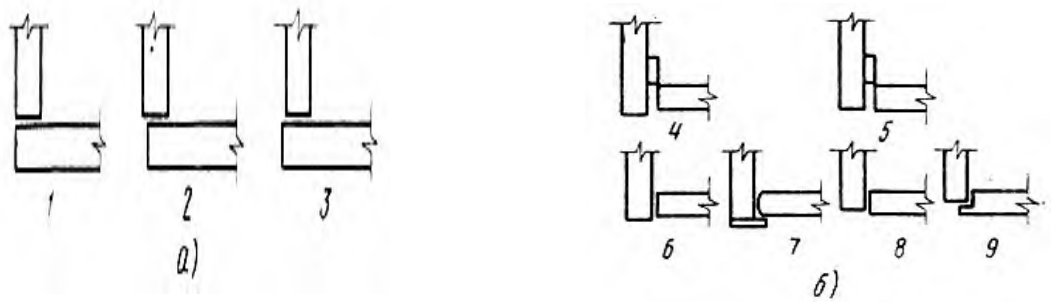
Схемы установки дверок к стенкам корпуса
